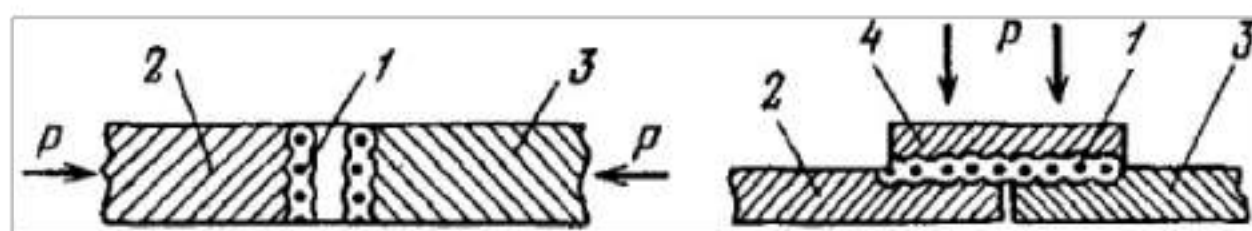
Схема зварювання нагрітим елементом, що залишається в деталі: 1 – нагрівальна спіраль, що залишається у зварному шві; 2, 3 – деталі, що зварюються; 4 – накладка
